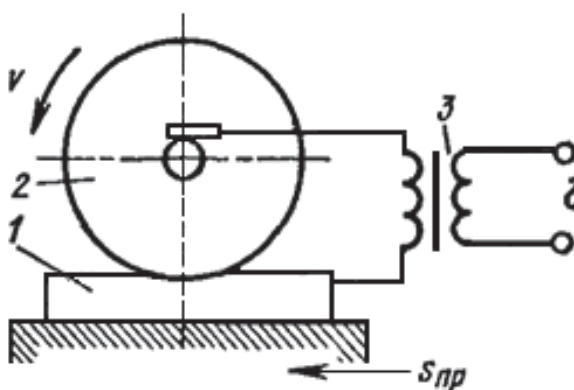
Схема електроконтактної обробки плоскої поверхні: 1 – оброблювана заготовка; 2 – інструмент-електрод; 3 – трансформатор
